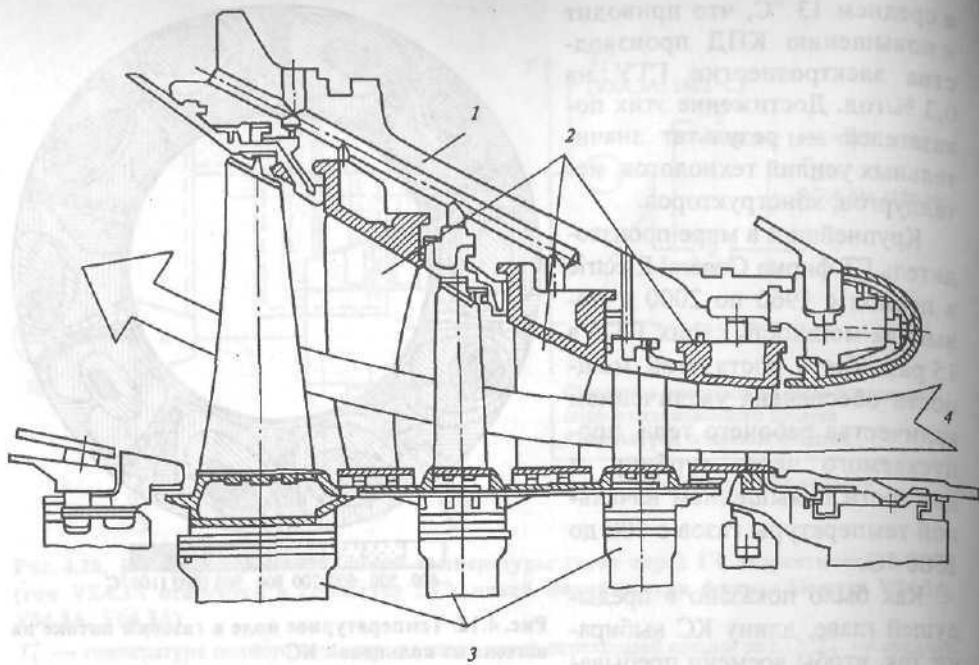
Пример конструктивной схемы проточной части ГТ (ГТУ типа GT8C фирмы АBB) 1 — несущая часть корпуса с каналами подвода охлаждающего воздуха; 2 — сопловые лопатки; 3 — рабочие лопатки; 4 — направление потока газов
